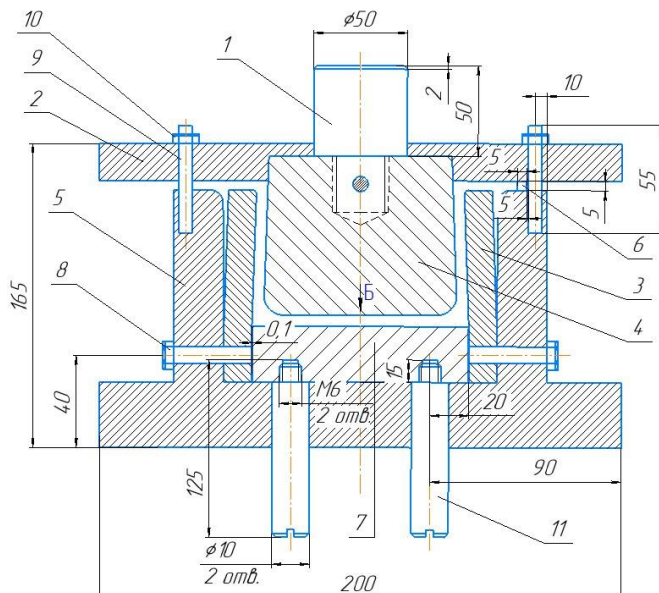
Схема штамповой оснастки: 1 – хвостовик; 2 – верхняя плита; 3 – упругие планки; 4 – пуансон; 5 – матрица и нижняя плита; 6 – упор; 7 – выталкиватель; 8 – болт; 9 – направляющие; 10 – гайка; 11 – выталкиватель
